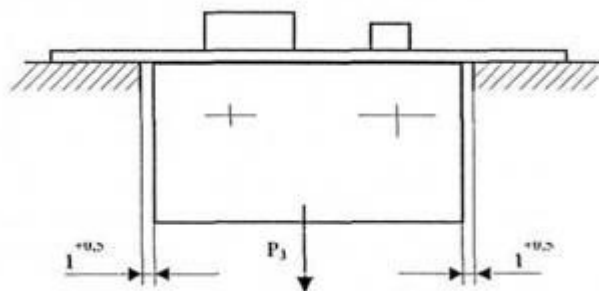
Схема випробувань зусиллям P_3 , з'єднання корпуса
